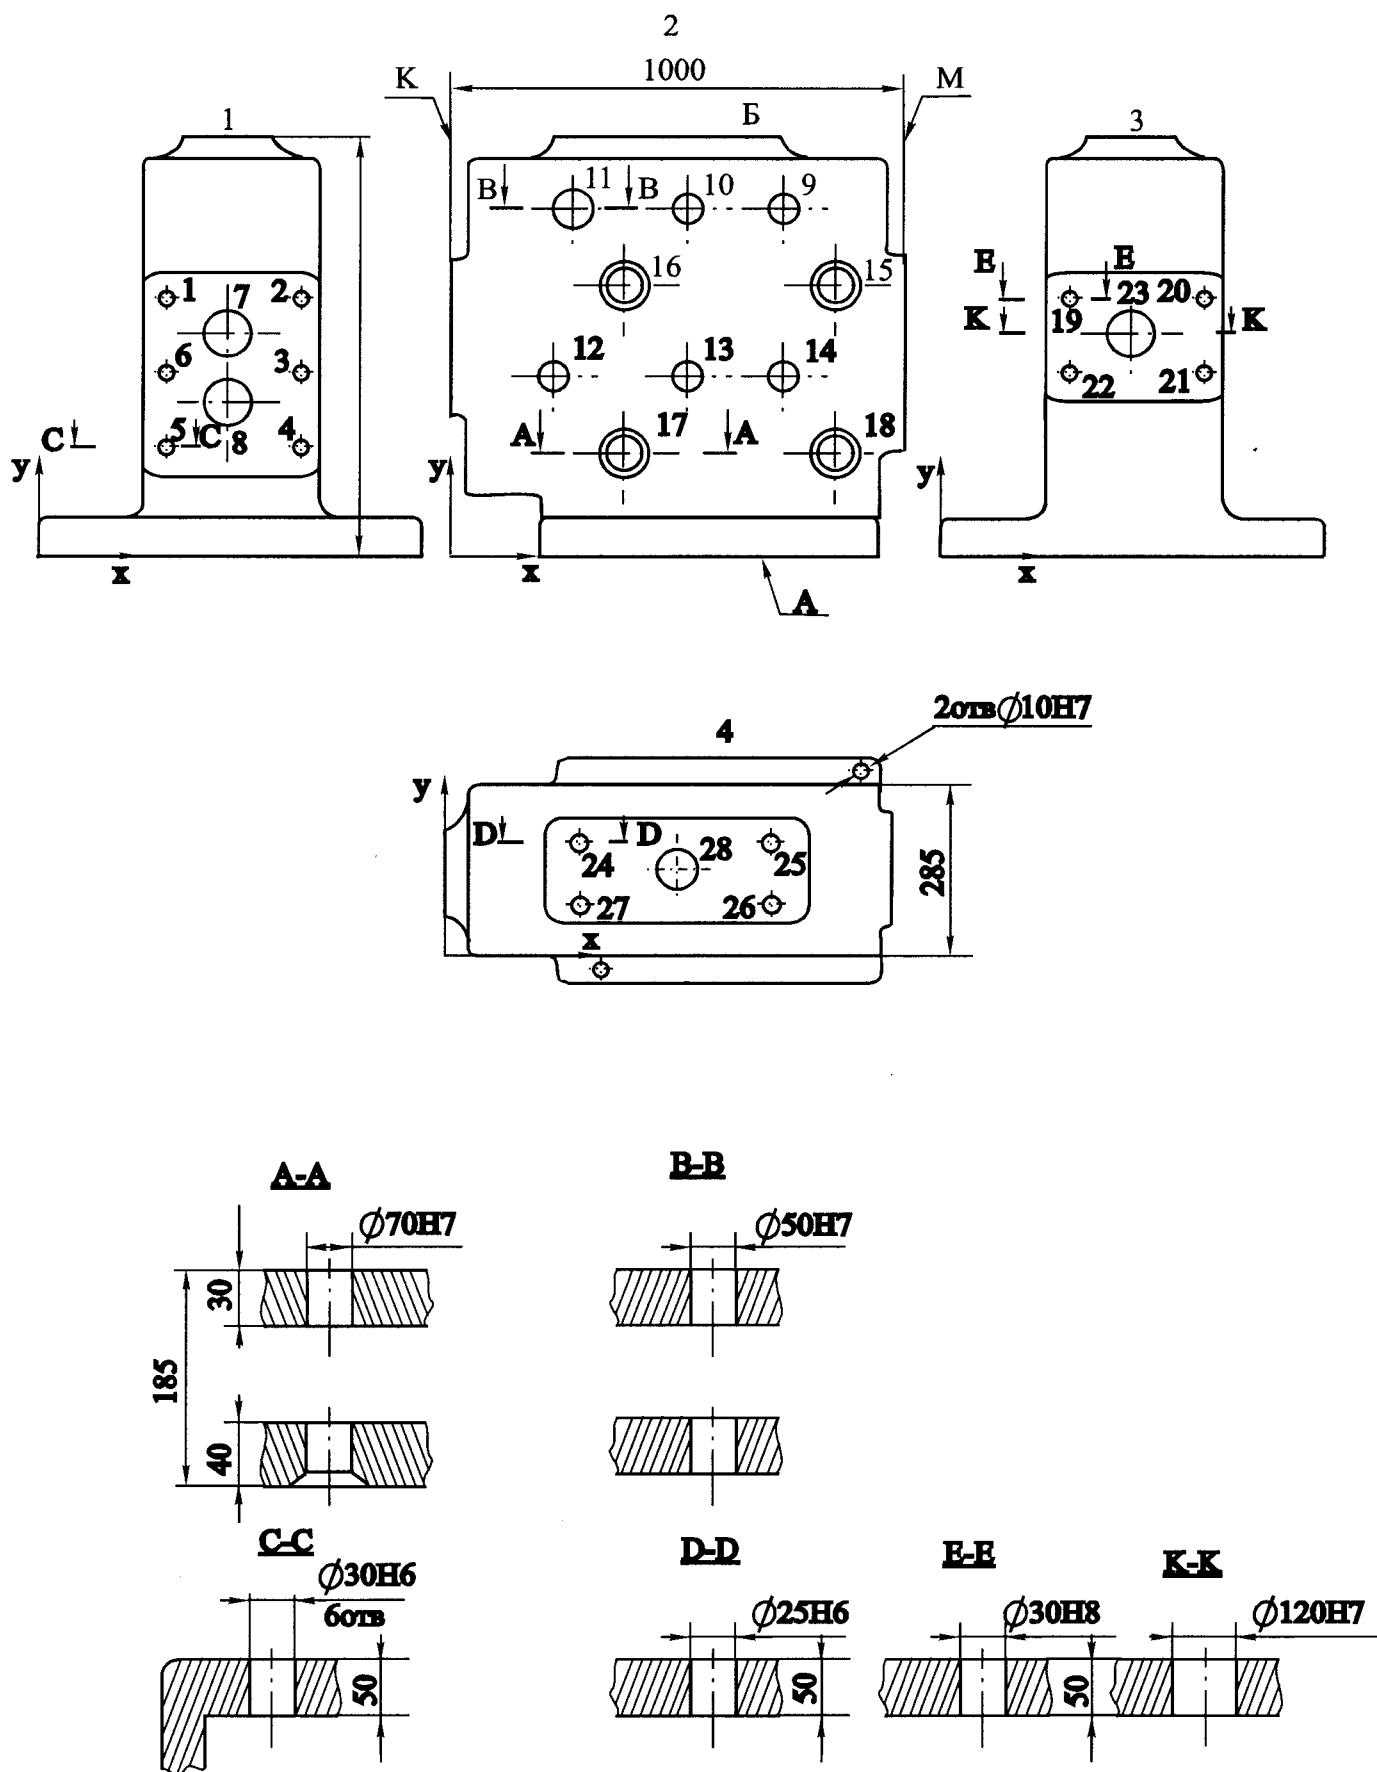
Розмірні схеми обробки отворів корпусної деталі.
